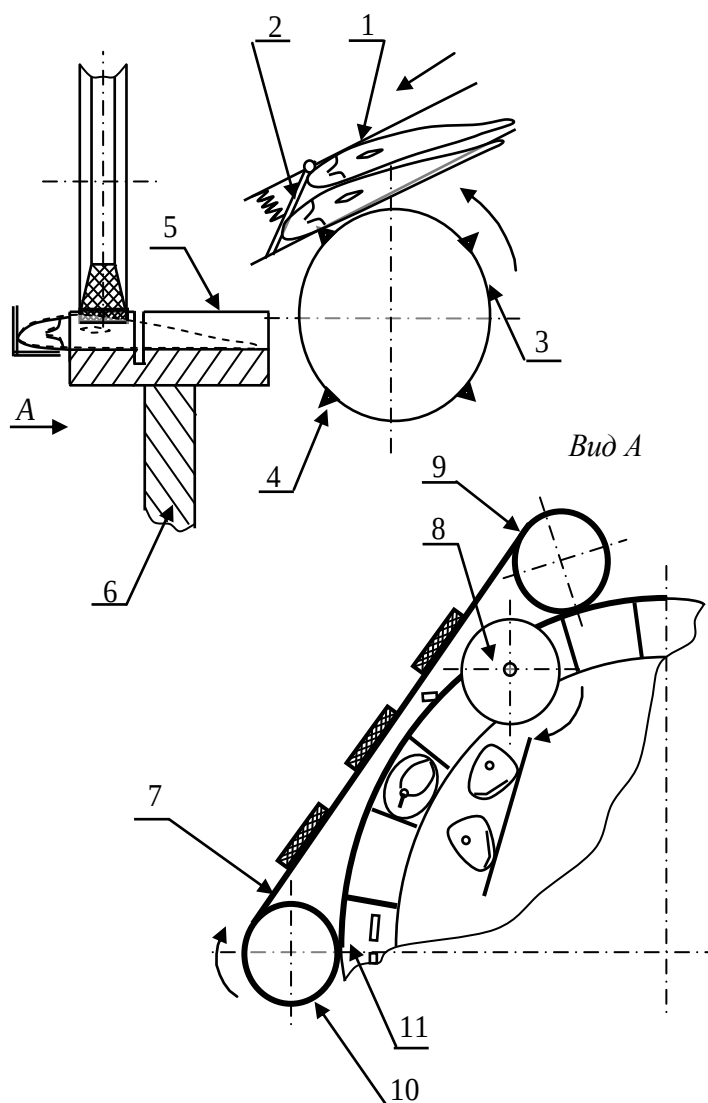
Схема конструкции рыботорной машины роторного типа
